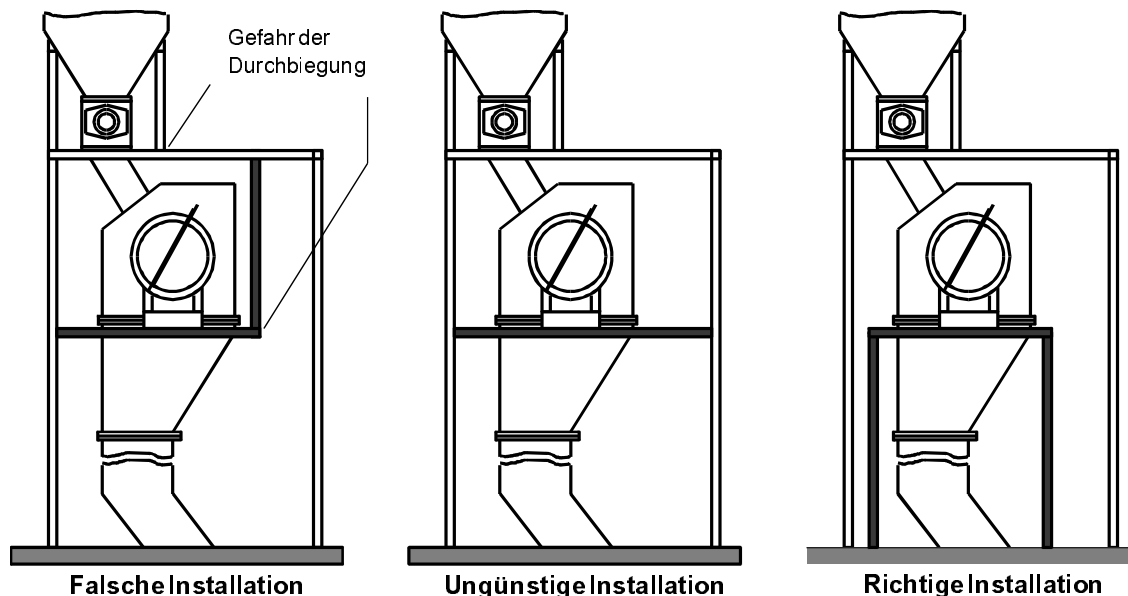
Bauseitige Unterkonstruktion für den Prallplattensensor
